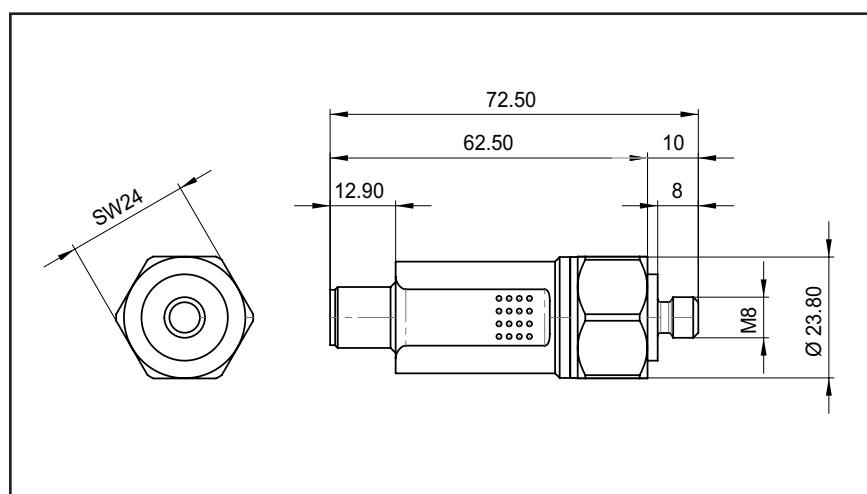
Gerät mit M12-Stecker, Abmessungen in mm
